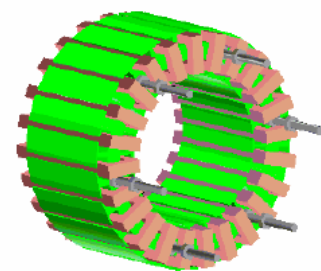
Bobinage Gramme pour machine à flux radial [16]
